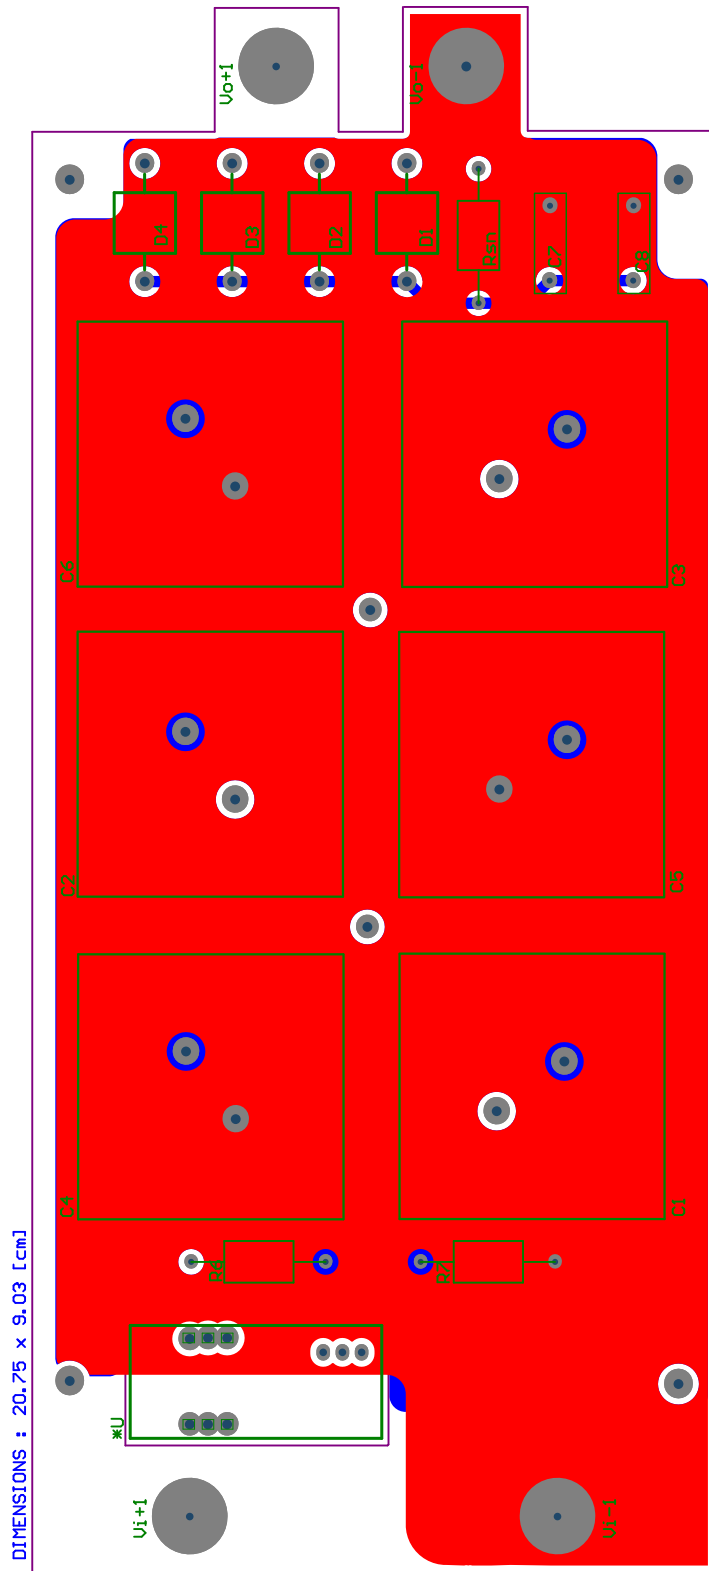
Layout da placa do barramento CC - BOTTOM Layer
